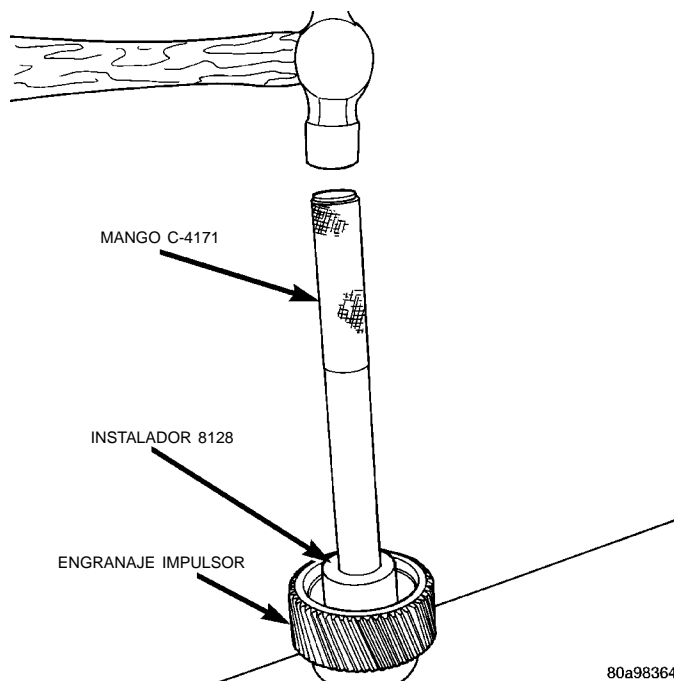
Instalación del cojinete de guía del engranaje impulsor
